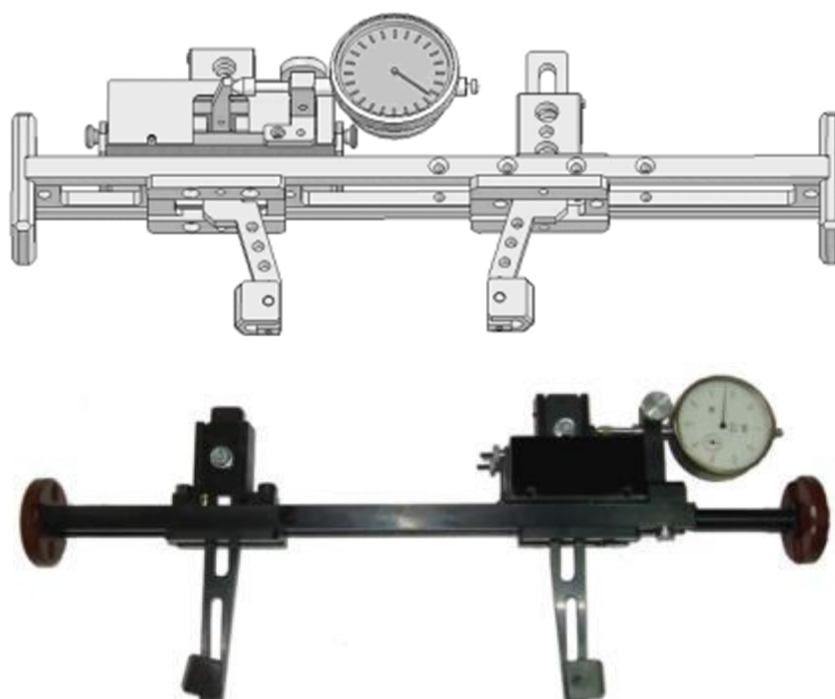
Типовые конструкции индикаторных приборов с КЭ ИН типа «сапожок»
